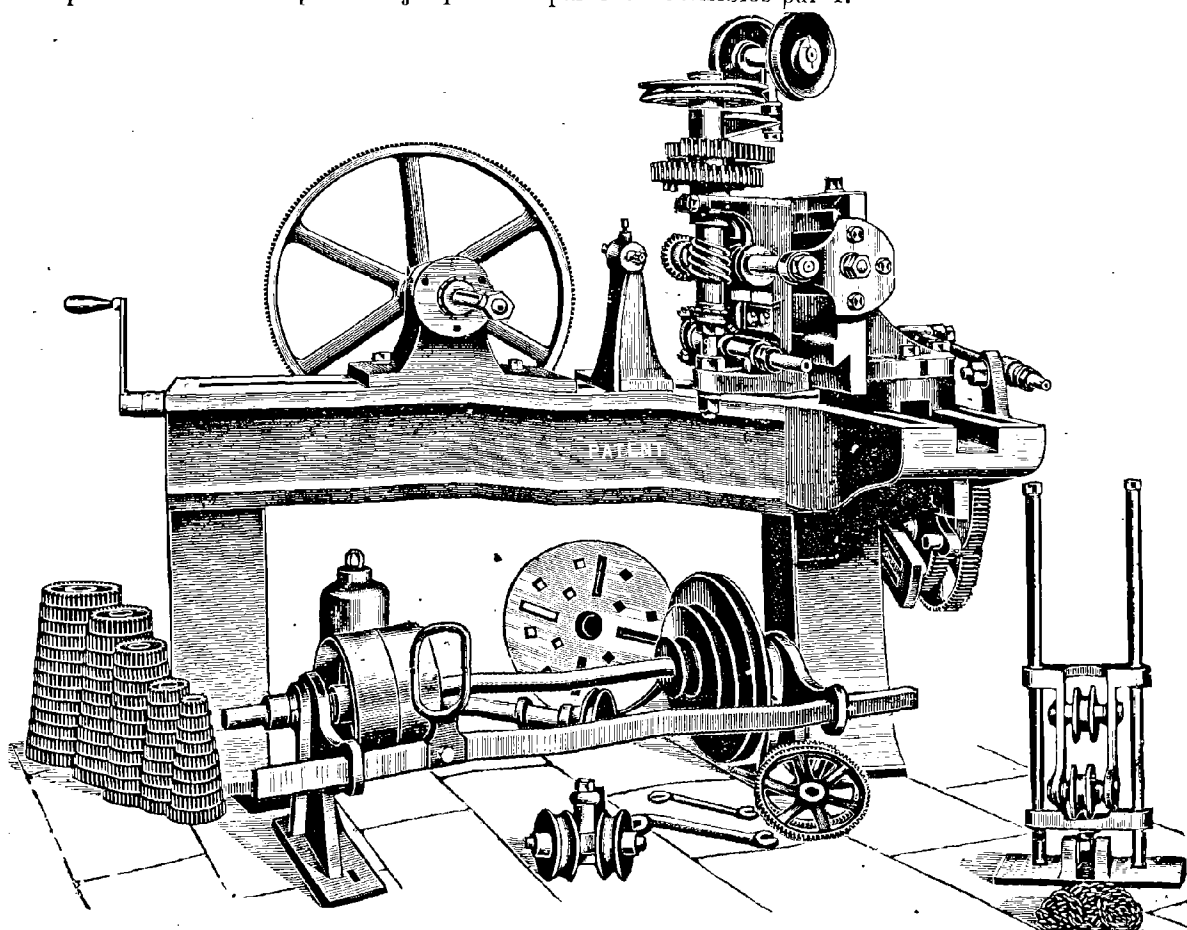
Machine automatique à diviser et tailler les engrenages de M. Lucas.
